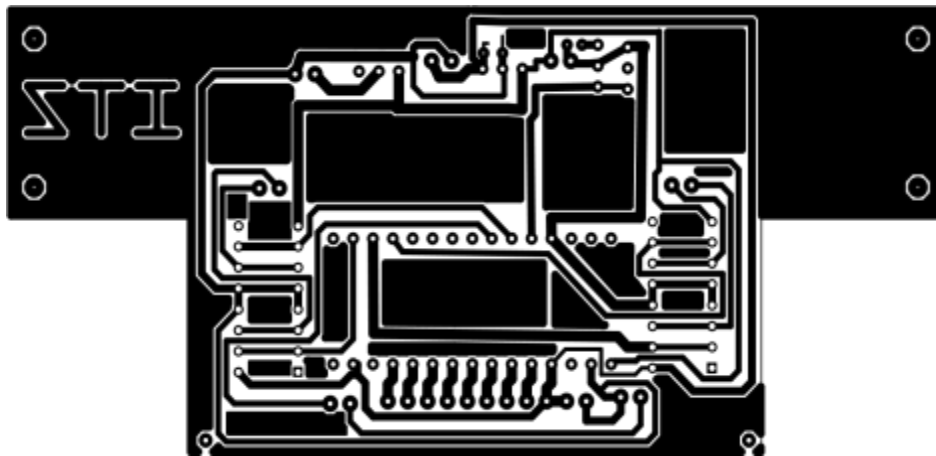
Dibujo de un pcb con el software de diseño Proteus.
